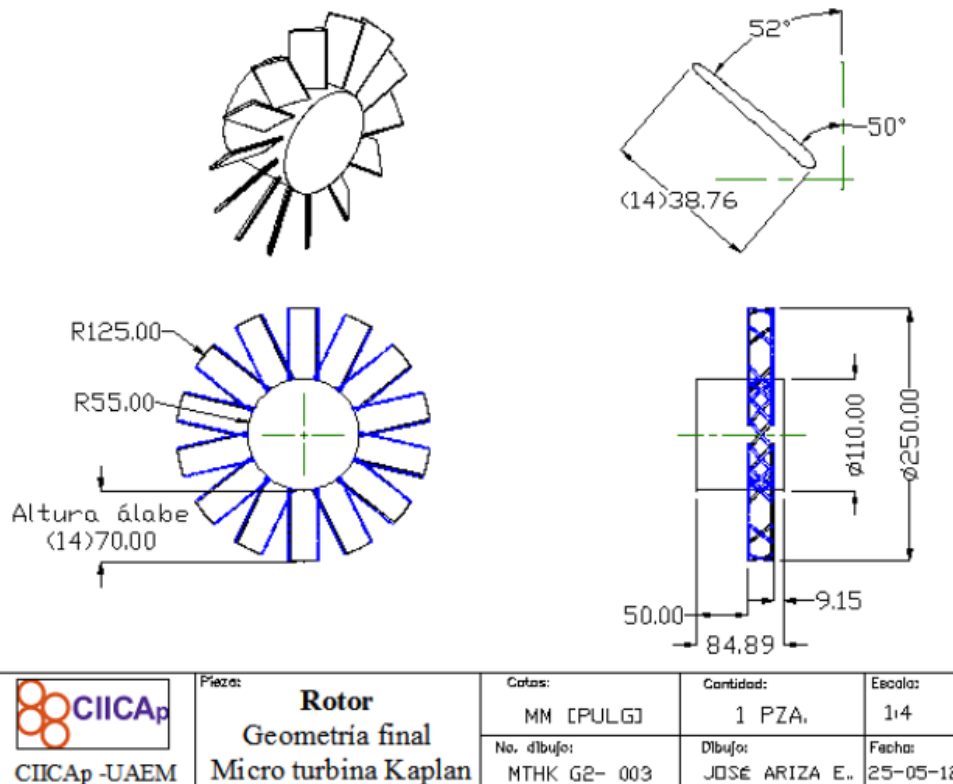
Dimensiones de la geometría del rodete en la microturbina hidráulica de flujo axial [22].
